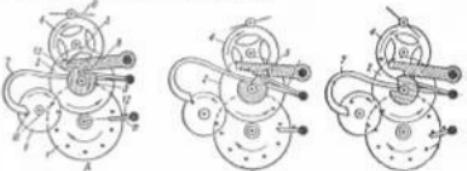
Схема работы механизма боя в замкнутом: положение Б—механизм боя во время подготовки к боя; А—механизм боя в действии; 1—подъемное колесо; 2—колесо с фигурированной шайбой; 3—фигурированная шайба; 4—стопорное колесо; 5—штифт стопорного колеса; 6—ветвька; 7—рычаг отмыкания; 8—тирач замыкания; 9—минутник; 10—шифты минутника; 11—колесо узла боя; 12—штифт упора; 13—колено рычага замыкания
